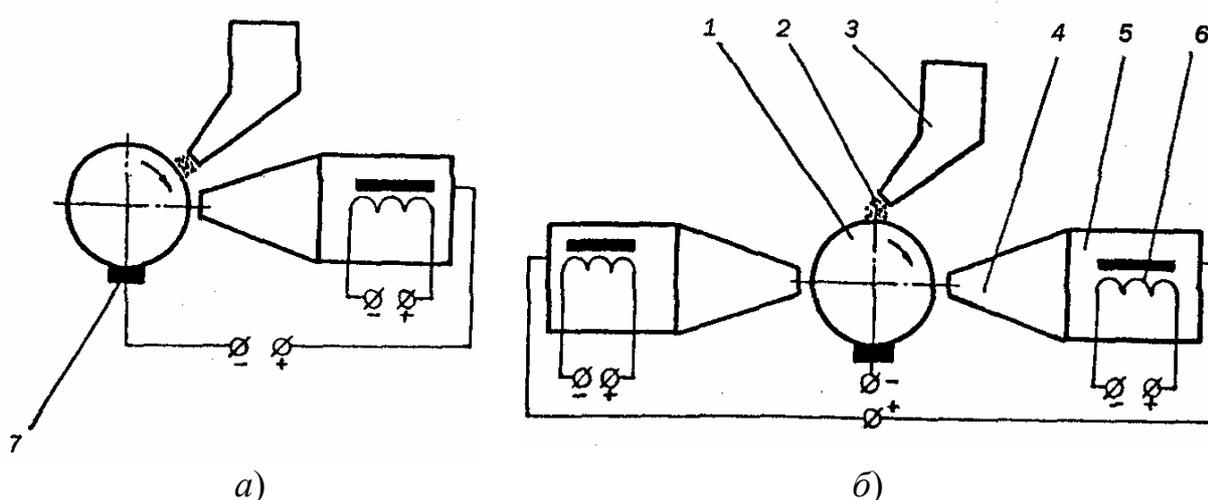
Схема электромагнитной наплавки: а – однополюсной; б – двухполюсной; 1 – заготовка, 2 – порошок, 3 – бункер, 4 – наконечник, 5 – корпус, 6 – электромагнит, 7 – щетка
